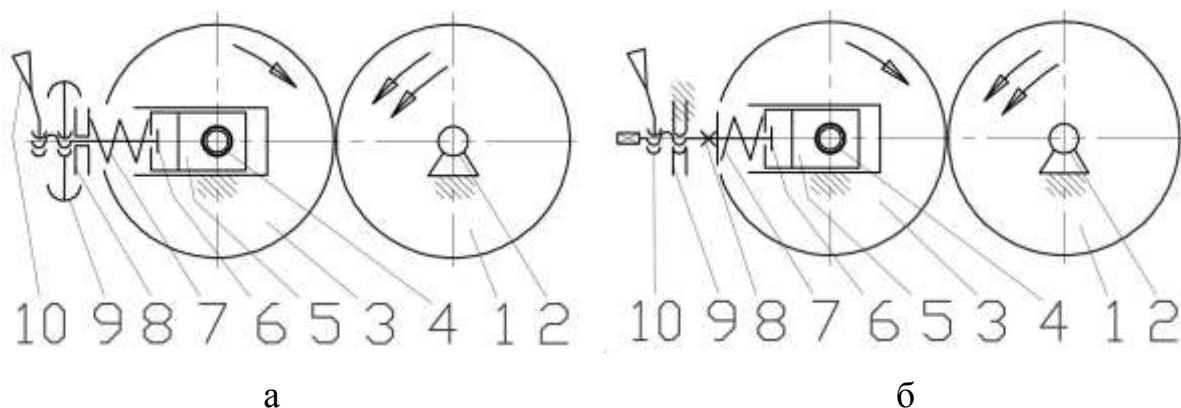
Схеми установчих механізмів вальцьових дробарок.
